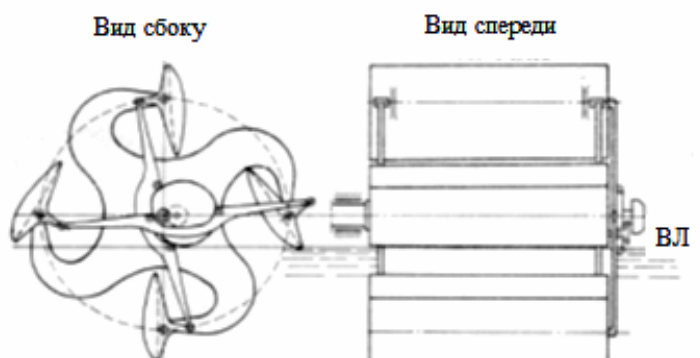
Схема рычажно-шарнирного высокооборотного гребного колеса
